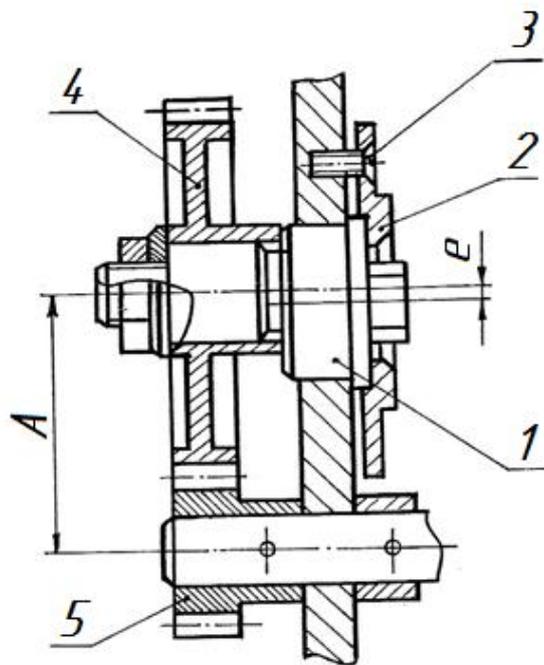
Передача с цилиндрическими зубчатыми колесами
